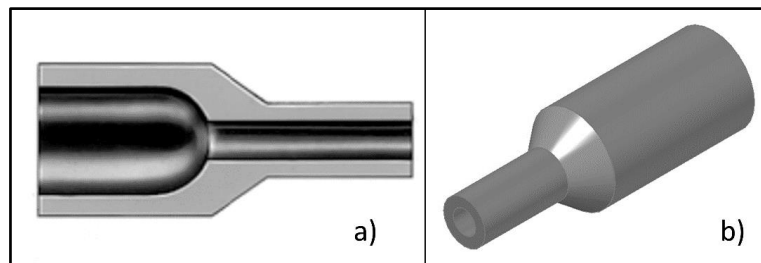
Redutor esquematizado (a) e em vista isométrica (b), [11] – “Weld Fittings”).
